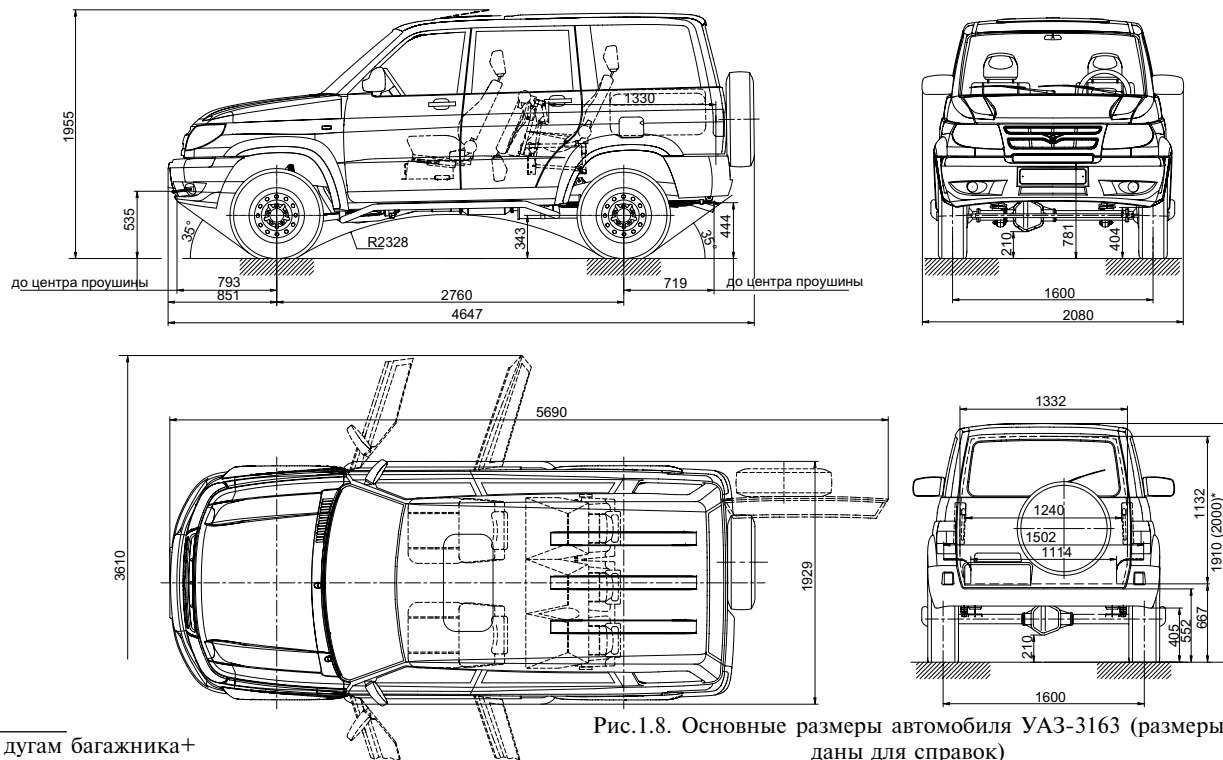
Основные размеры автомобиля УАЗ-3163 (размеры даны для справки)
